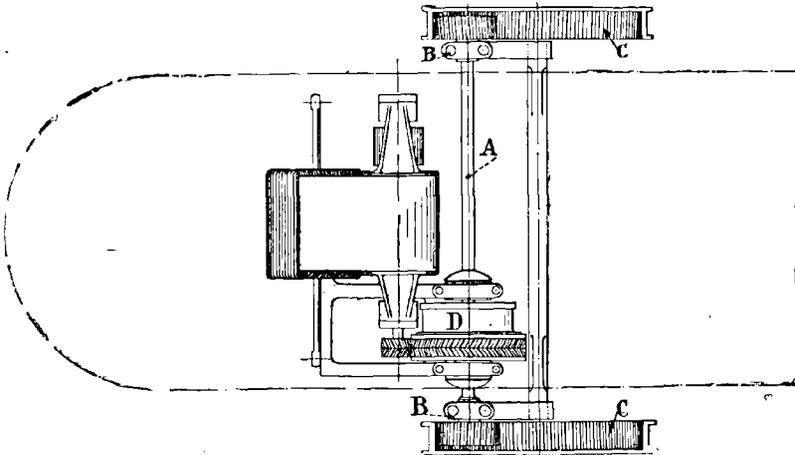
Première voiture Jeantaud (1881). — Plan.
